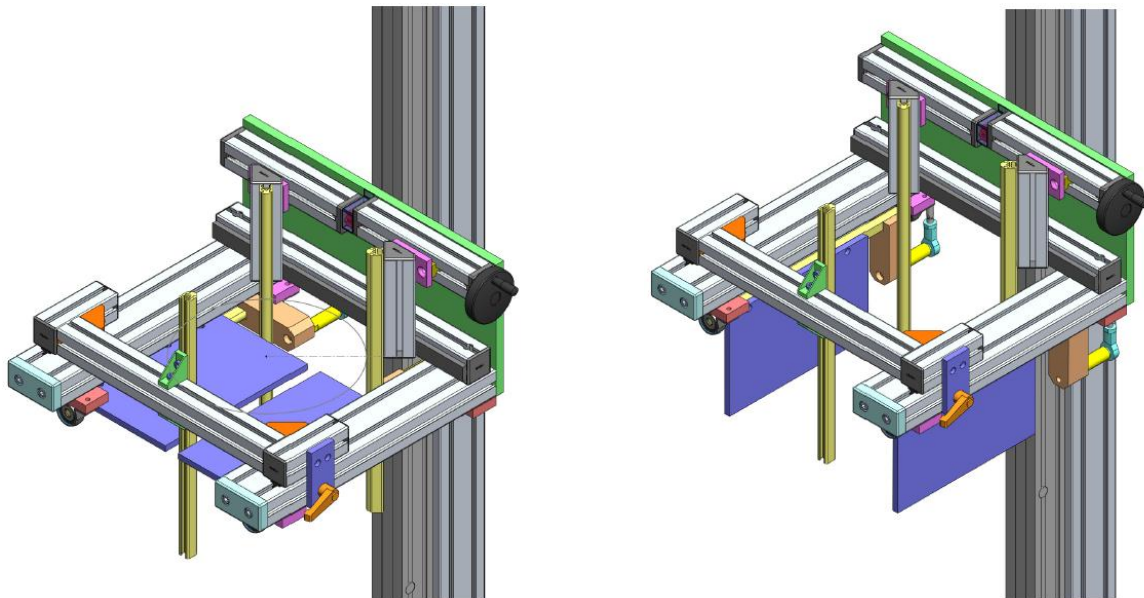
Vista isométrica do sistema com representação da embalagem “antes de ser largada” – à esquerda; Vista isométrica do sistema com representação da embalagem “depois de ser largada” – à direita
